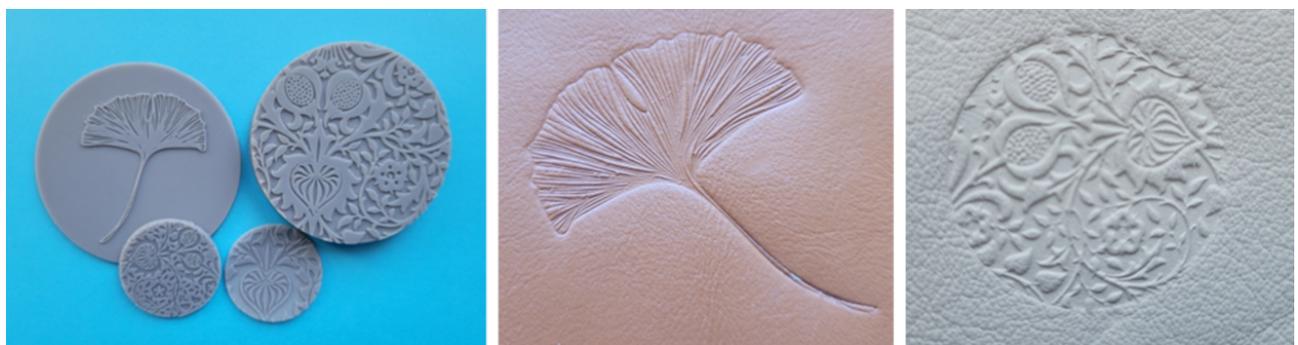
Beispiele für Kunststoffprägewerkzeuge und Ultraschallprägungen
